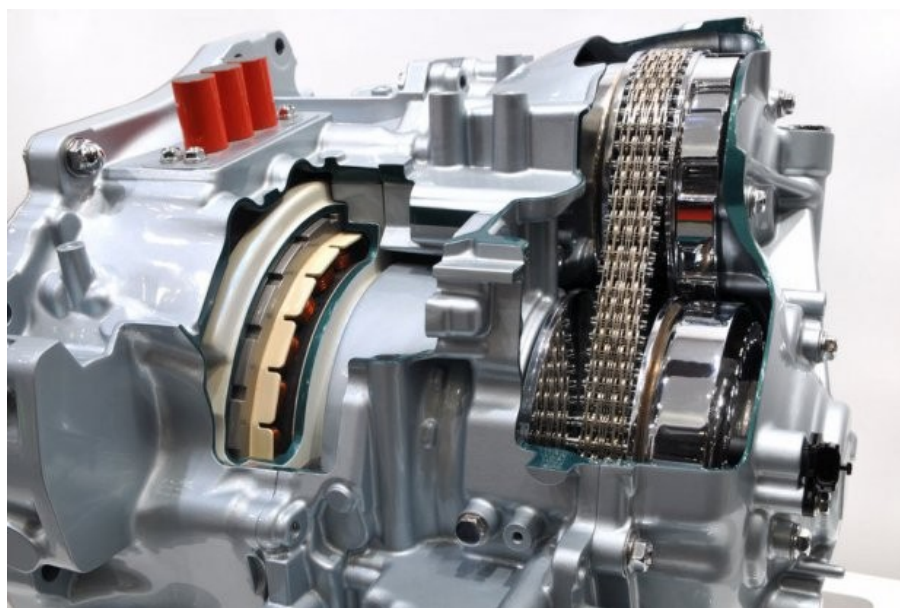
Загальний вигляд варіаторної КПП
